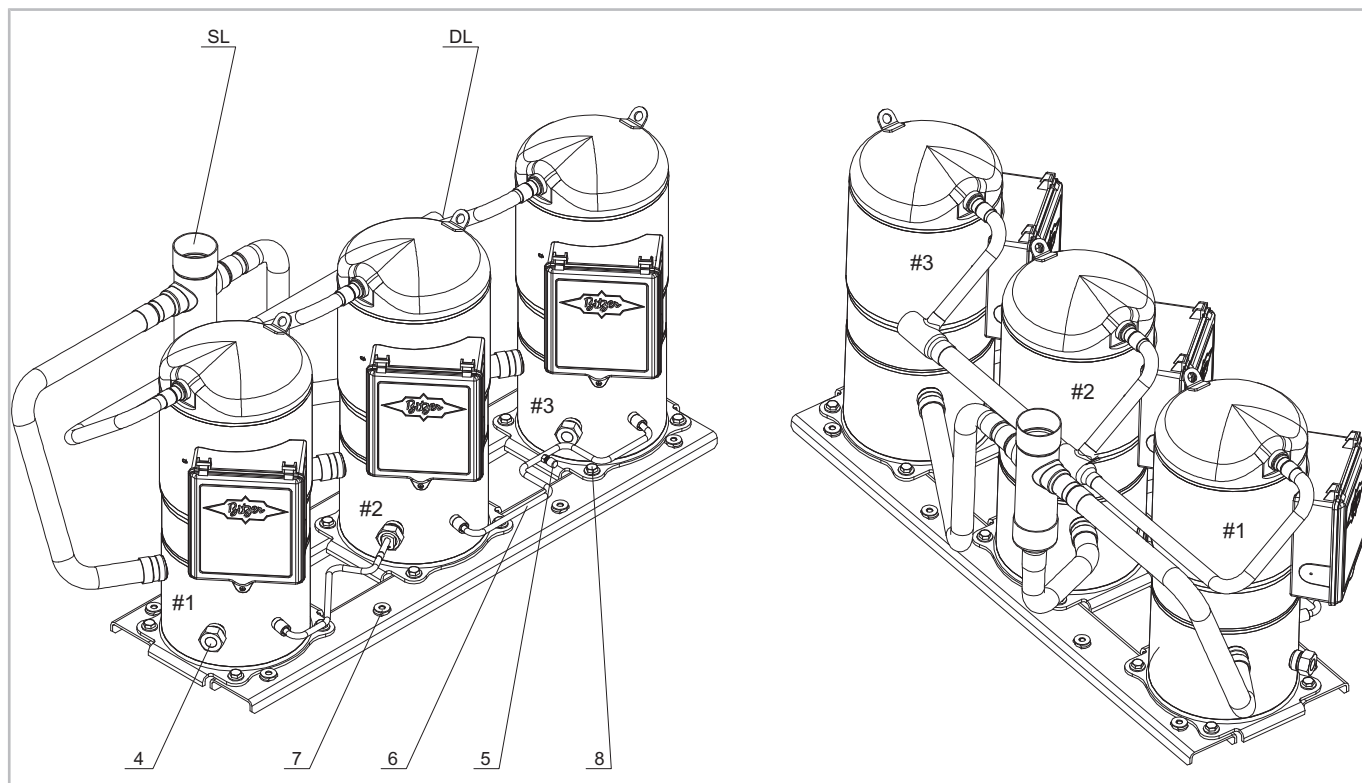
Пример равного трио объединения компрессоров ORBIT 6 с BITZER Advanced Header Technology (вертикальный BAHT header)
